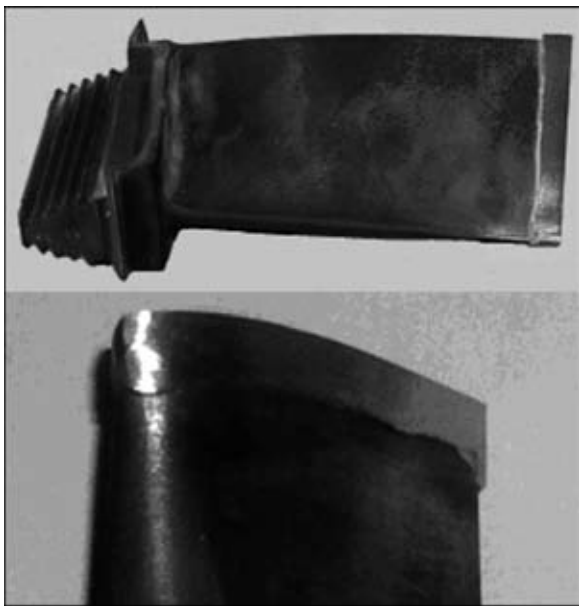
Внешний вид лопаток газовых турбин, восстановленных сваркой
